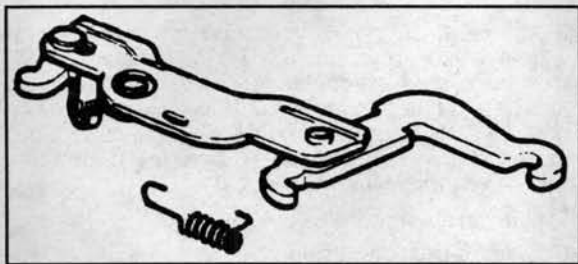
Детали механизма автоматической регулировки зазора тормозов автомобилей с двигателями В13/В14, В172, D16
